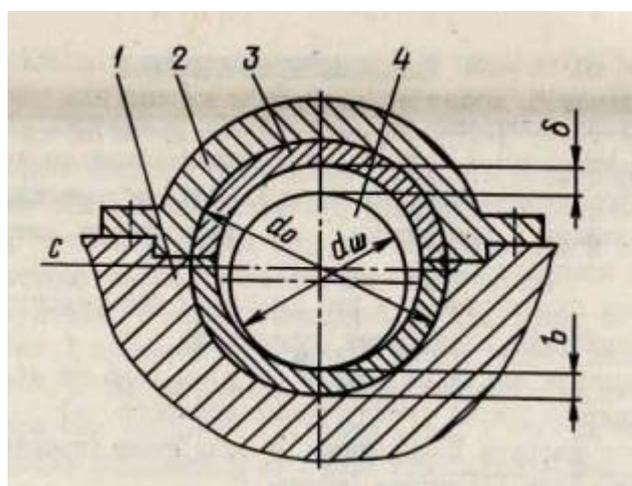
Проверка зазоров в подшипниках с тонкостенными вкладышами:
